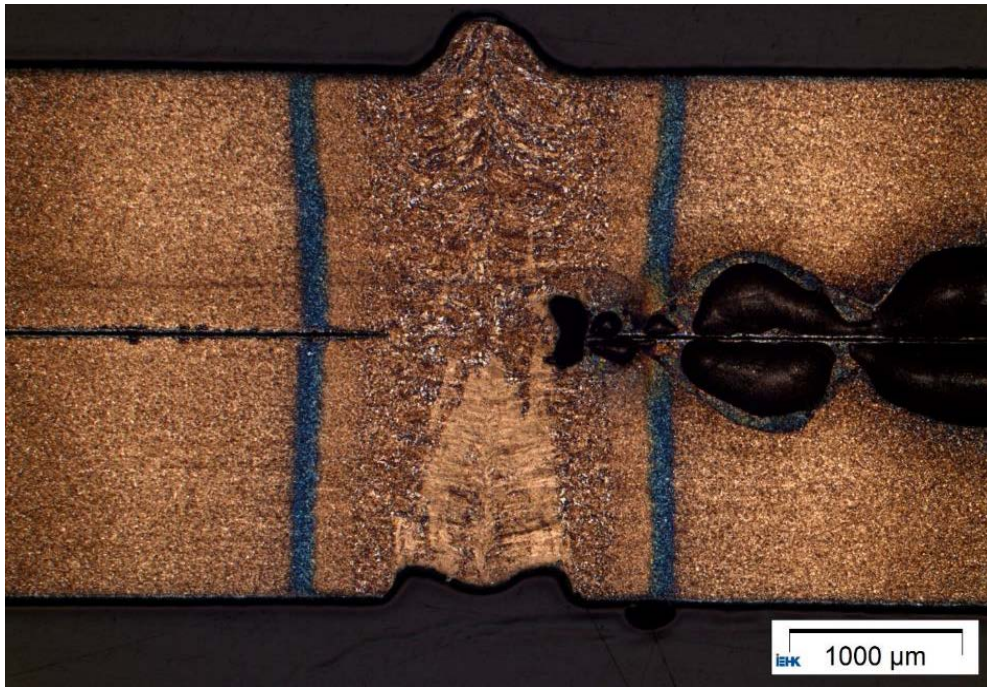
Überblick der mittels Laserstrahl geschweißten Schweißnaht des Probenpaares 279+280, Klemmätzung.
